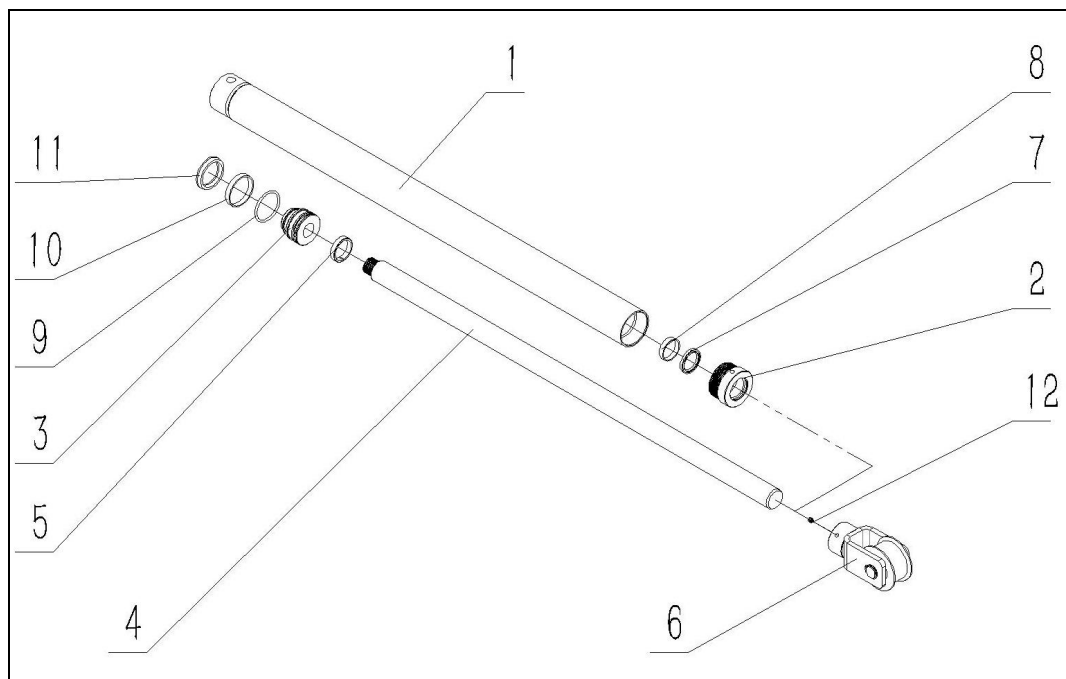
Disegno esploso del cilindro idraulico del sollevatore
